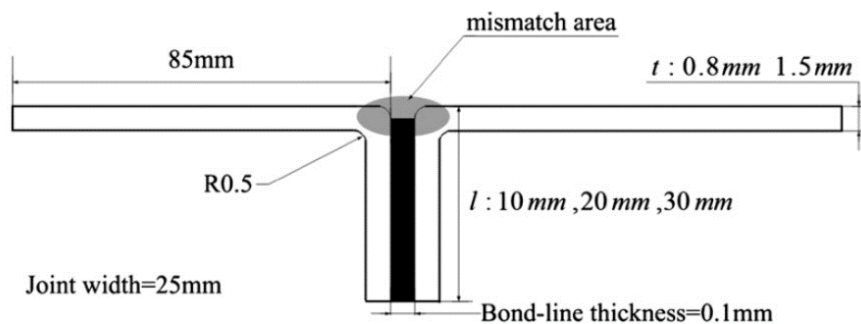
Geometria e dimensões da junta T em estudo [52].
